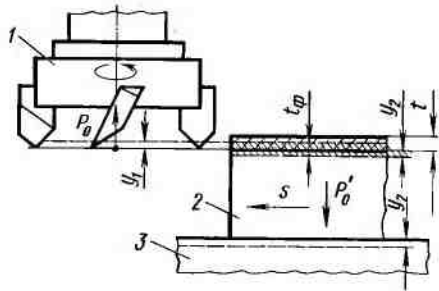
Схема упругих перемещений при фрезеровании торцевой фрезой
